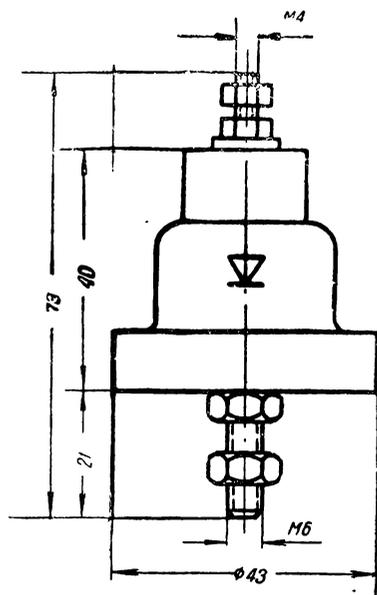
Габаритные размеры германиевого вентиля ВГ-10
